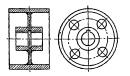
Ротор сипхронной машины виде сварного магинтного колеса.
